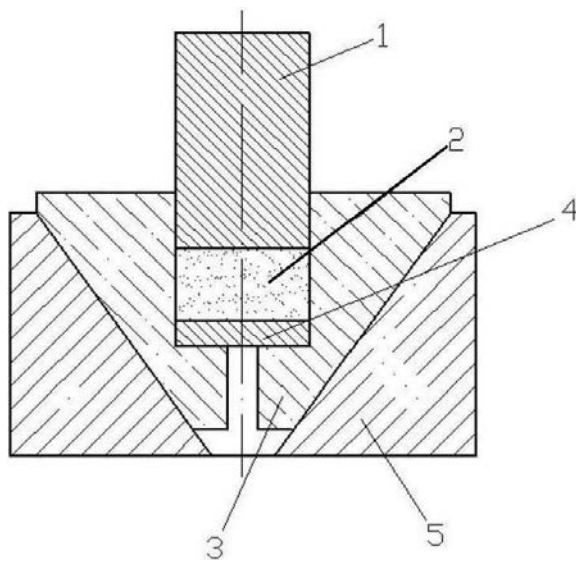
Схема пресс-формы для получения брикетов под последующую совмещенную прокатку-прессование: 1 – верхний пуансон, 2 – стружка, 3 – матрица, 4 - нижний пуансон, 5 - обойма
